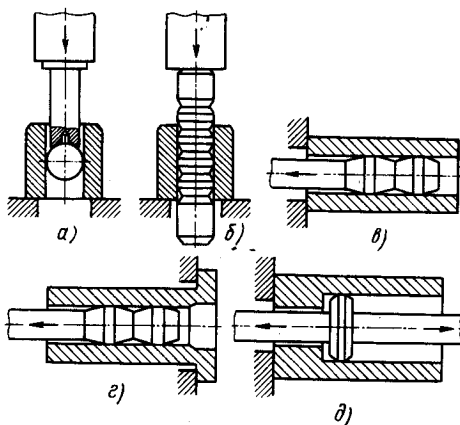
Схемы обработки отверстий: а и б – прошиванием с помощью шарика и оправки; в – со сжатием детали; г – с растяжением детали; д – при возвратно-поступательном ходе оправки
